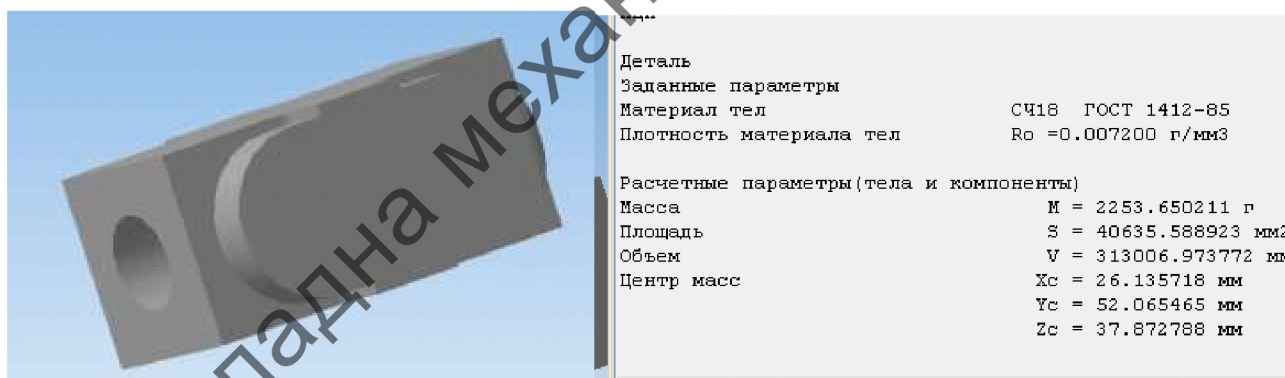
Визначення маси заготовки для лиття в піщано-глинисті форми з машинним формуванням
